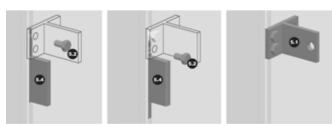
Vier T-Stücke (5.1/ 6.1) je Kollektor mit Sechskantschrauben M8 (5.2/ 6.2) an den Vierkantmuttern in der Nut auf der Kollektorrückseite vormontieren. Dazu die erste Vierkantmutter mit Hilfe der langen Seite der Montagehilfe ausrichten. Das T-Stück ansetzen und eine Sechskantschraube einschrauben. Durch drehen der Montagehilfe die zweite Vierkantmutter ausrichten und eine weitere Sechskantschraube einschrauben.
